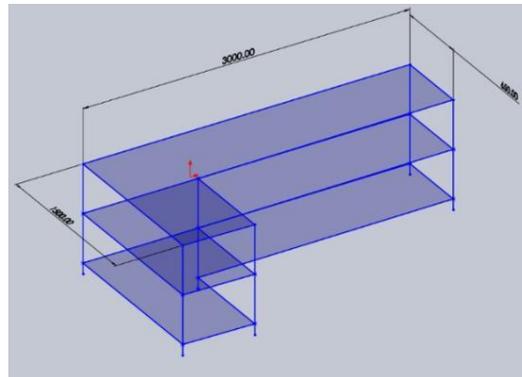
6 Área de entradas Fuente: Elaboración propia
